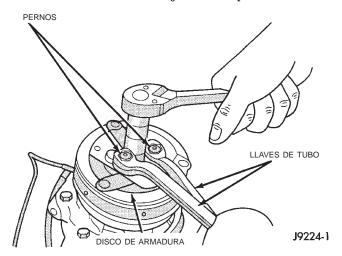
Desmontaje e instalación de la tuerca del eje del compresor
